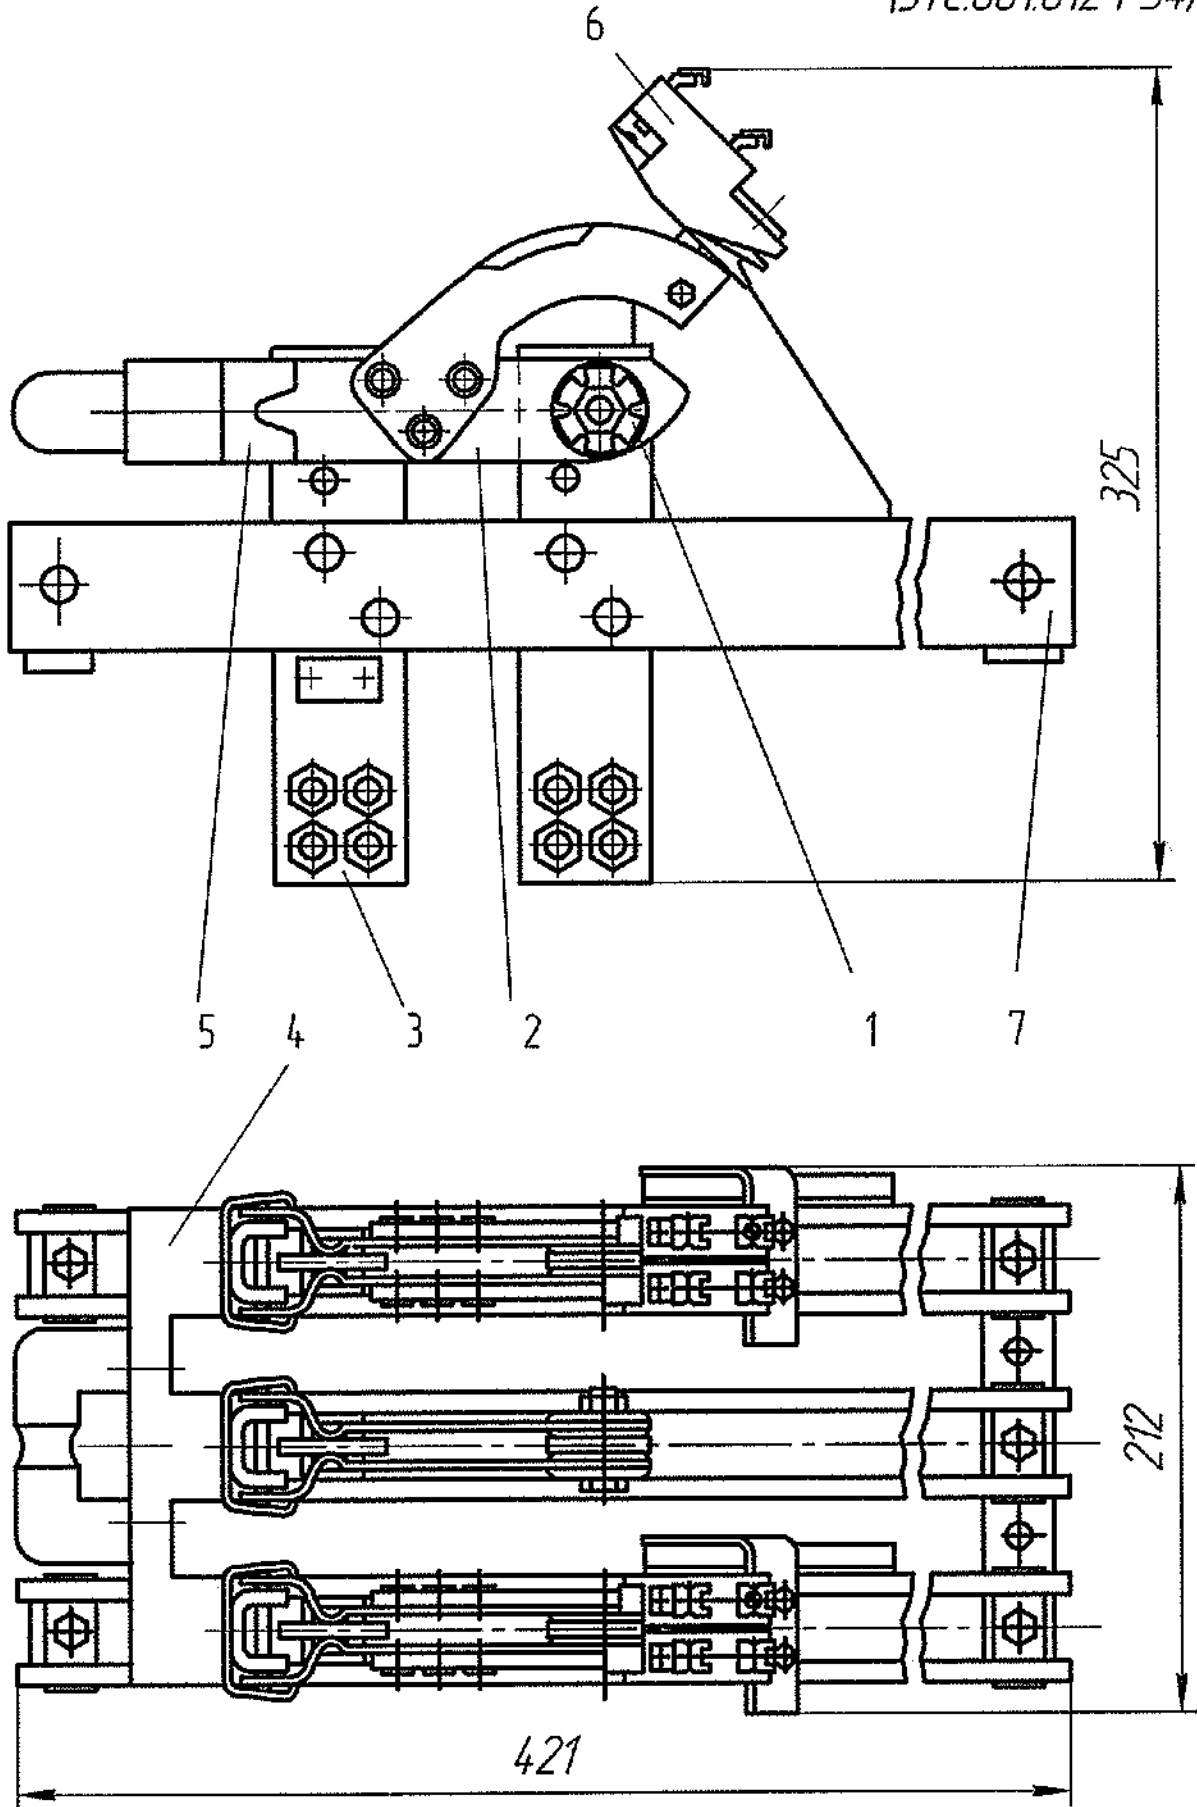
Разъединитель вентиляного двигателя РВД-58
